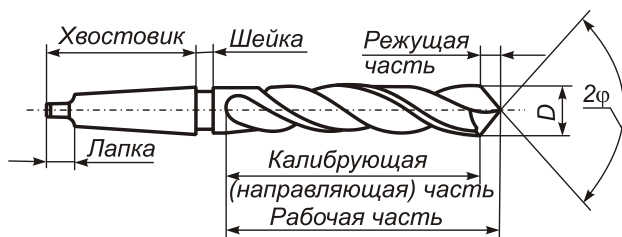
Общий вид и основные элементы конструкции винтового сверла
